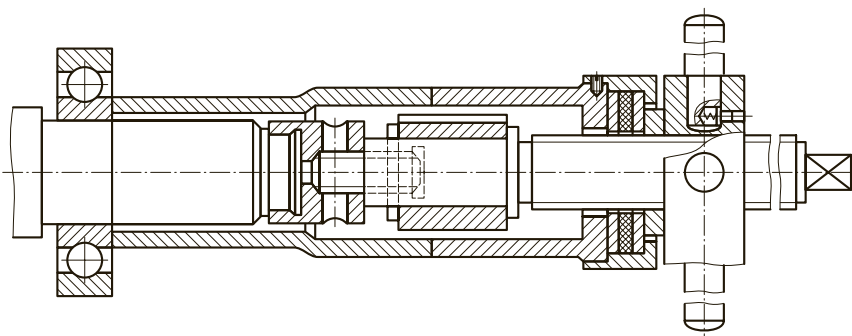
Приспособление с винтовым приводом для напрессовывания подшипника качения на вал
